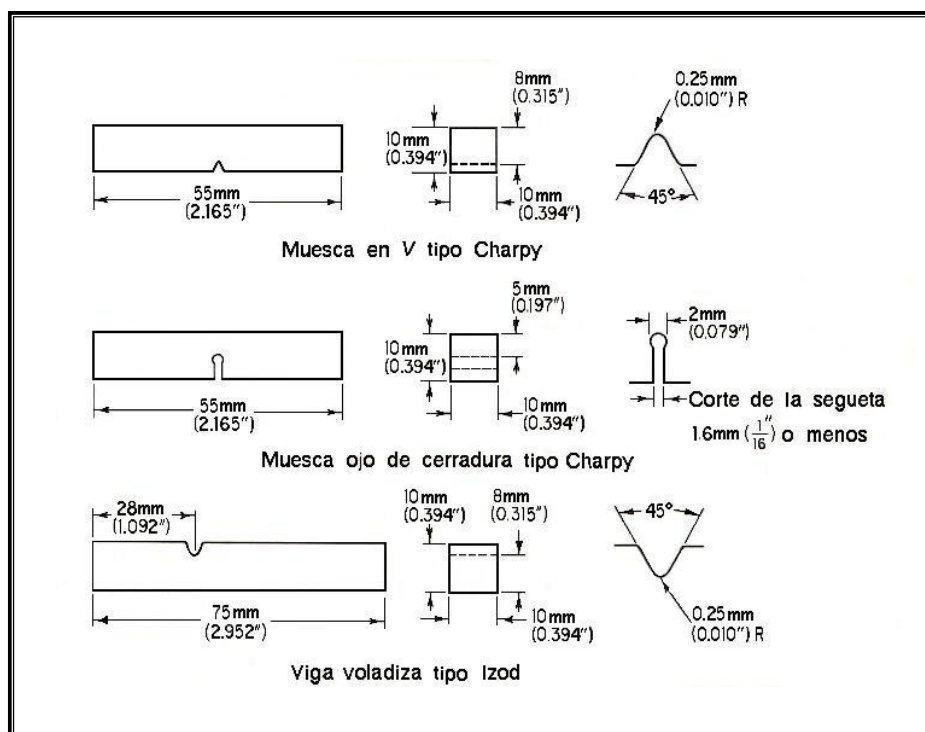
PROBETAS CHARPY E IZOD DE UN ENSAYO DE IMPACTO (4)
